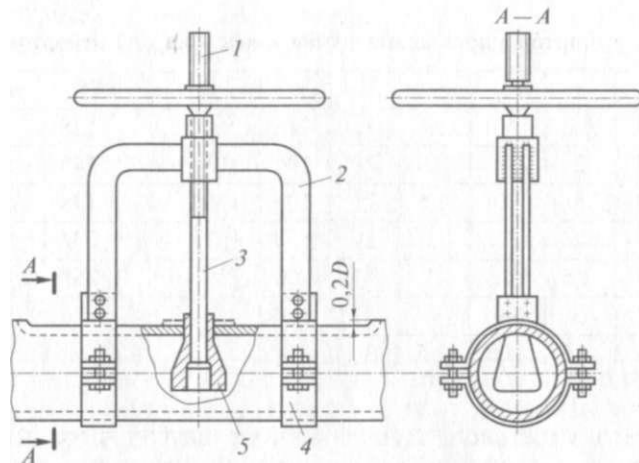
Винтовое приспособление для вытяжки ответвлений в трубах:
